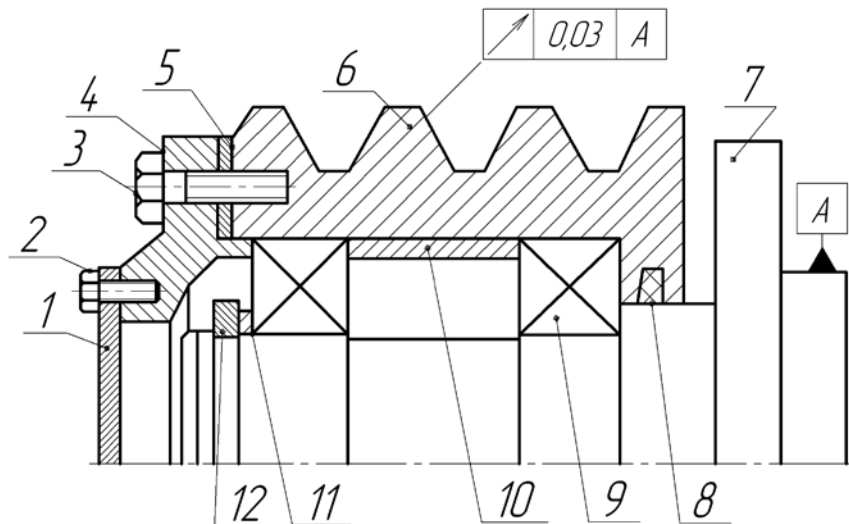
Эскиз ступицы в сборе: 1 – крышка; 2,3 – винты; 4 – фланец; 5 – прокладка; 6 – шкив; 7 – ступица; 8 – кольцо уплотнительное; 9 – подшипник; 10 – втулка; 11 – кольцо компенсационное; 12 – кольцо стопорное
